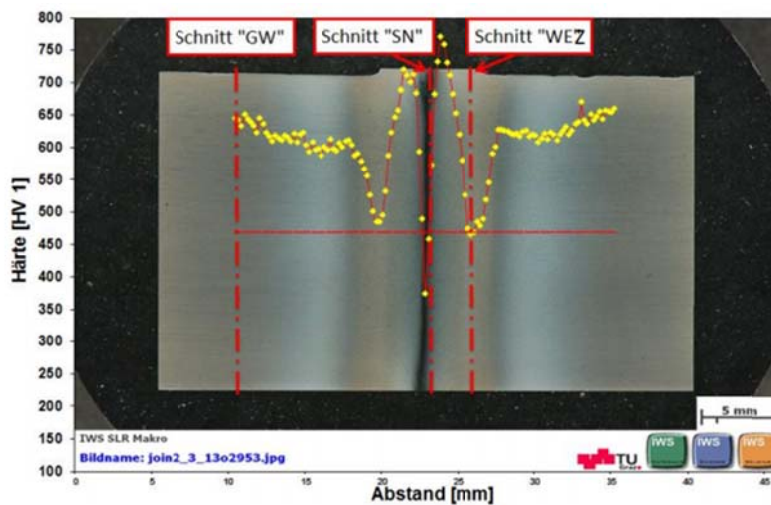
Härteverlauf HV1 eines linearreibgeschweißten 1.4112 Kettengliedes [4]
